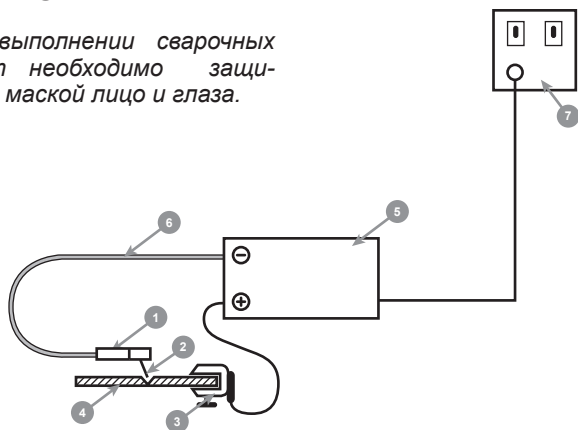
Схема подключения сварочного инвертора в режиме ММА-сварки.
